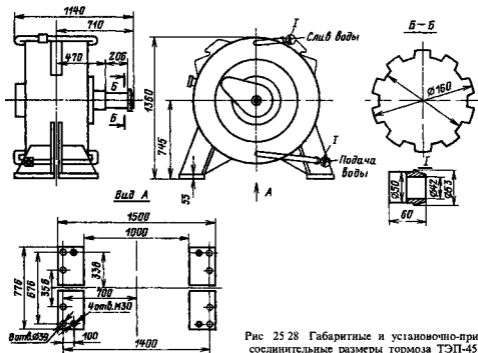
28 Габаритные и установочно-присоединительные размеры тормоза ТЭП-45
